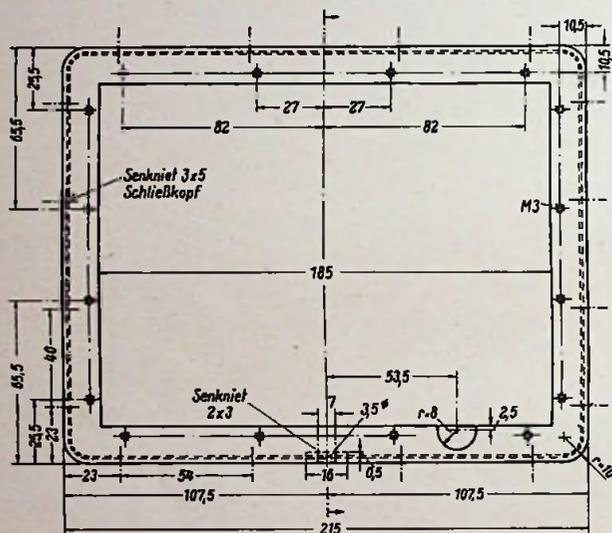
Gehäuse; Werkstoff: Tiefziehblech St. 37.21, Oberfläche: grauer Schruppflack
